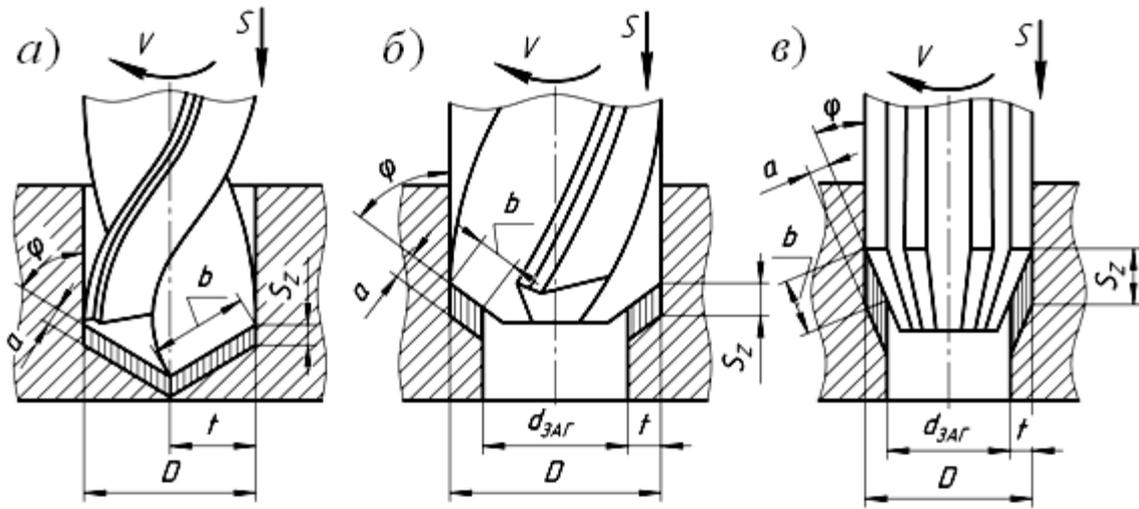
Схемы процессов сверления (а), зенкерования (б) и развертывания (в)
